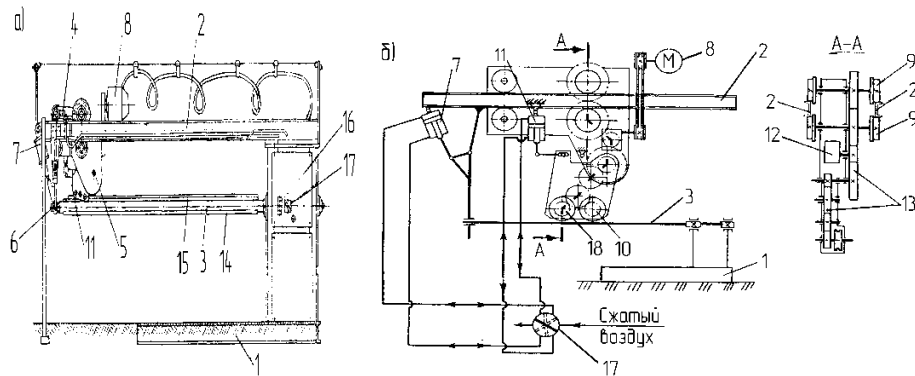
Фальцеосадочный станок: а) - общий вид; б) - кинематическая схема; - рама; 2 - верхняя балка; 3 - балка-матрица; 4 - самоходная головка; 5 - каретка; 7 - пневмоцилиндр замкового устройства; 8 - электродвигатель; 9 - колеса самоходной головки; 10, 18 - осаживающие ролики; 11 - пневмоцилиндр; 12 - червячный редуктор; 13 - промежуточная зубчатая передача; 14 - плоская планка; 15 - призматическая планка; 16 - кнопочный пульт; 17 - воздушный кран
